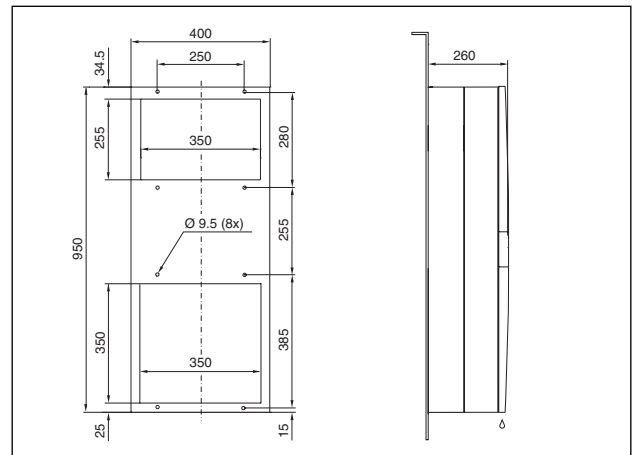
SK 3304.xxx, SK 3305.xxx Påbyggnad
